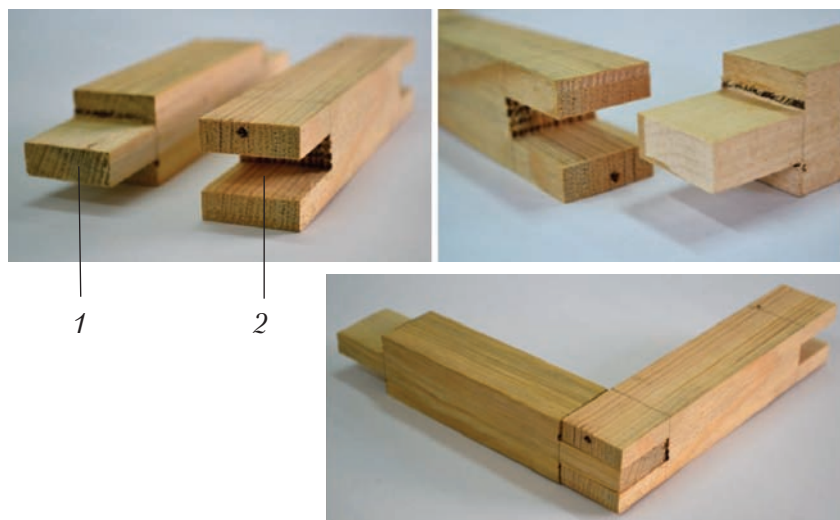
Шипове з'єднання: 1 – шип; 2 – вушко
